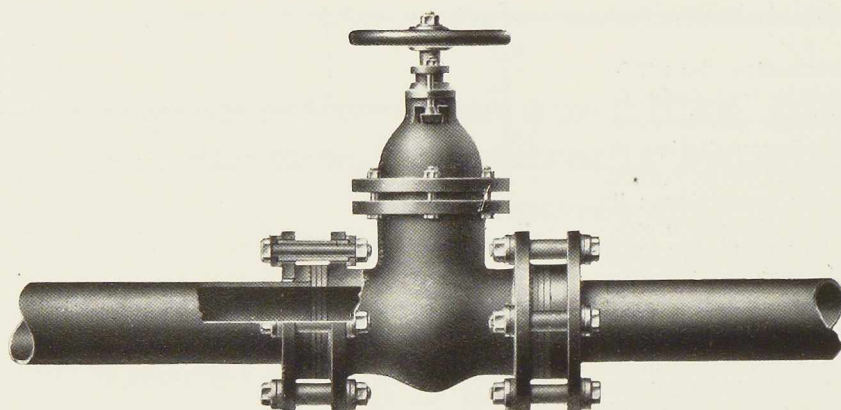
Isolement des assemblages à brides au droit d'une vanne.
